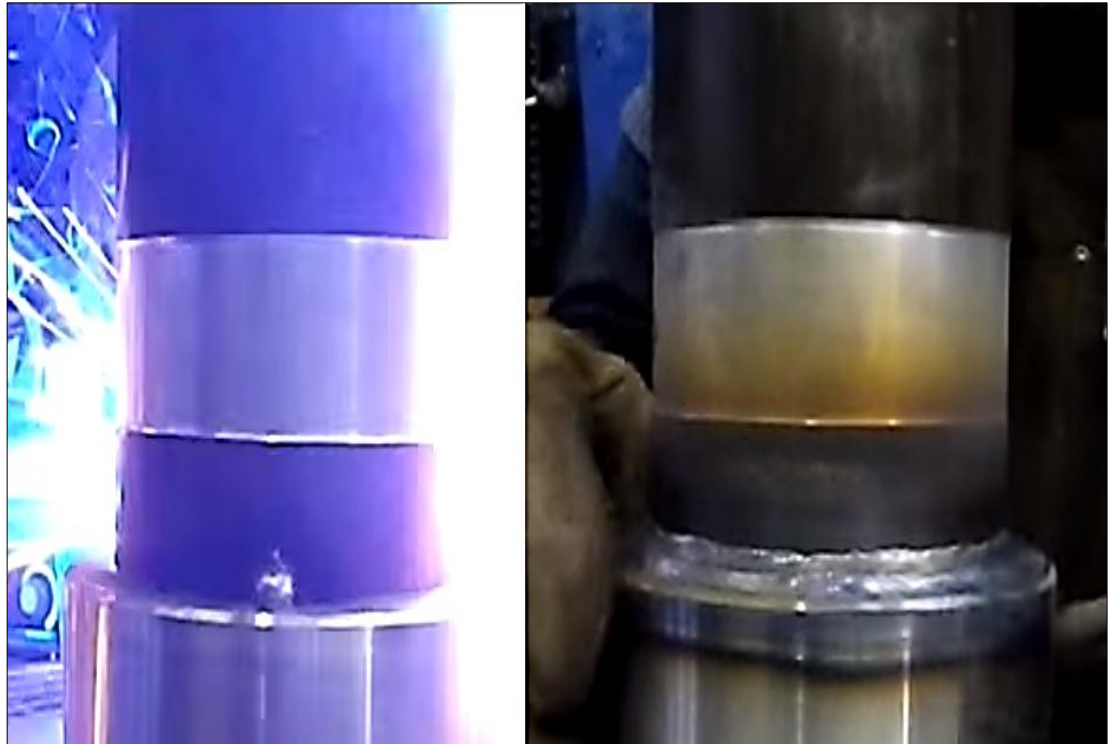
Punteado y cordón de soldadura de la brida
